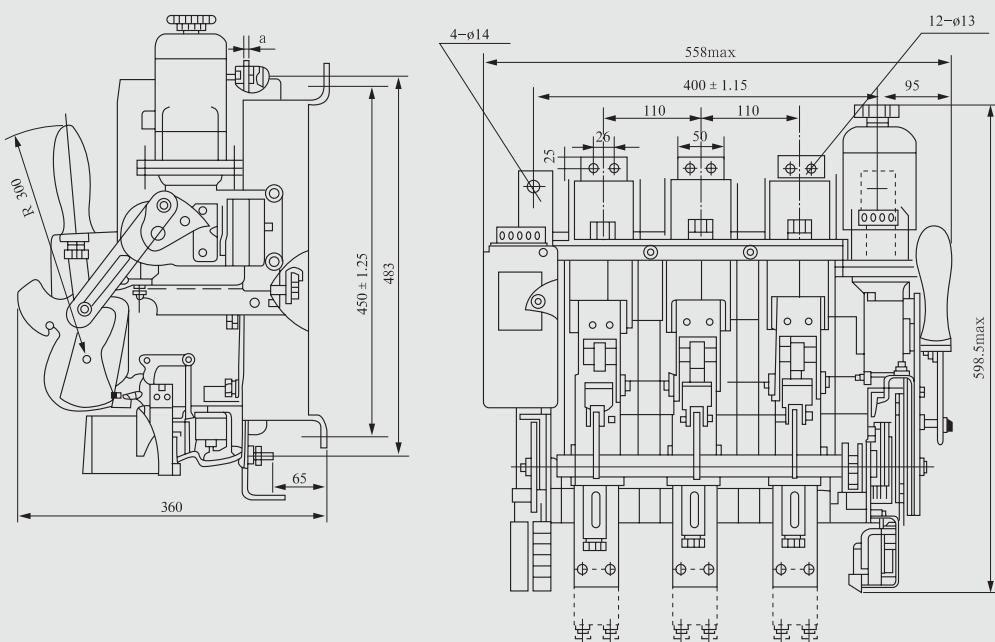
DW16-2000 直接手柄操作及电动机操作外形及安装尺寸
